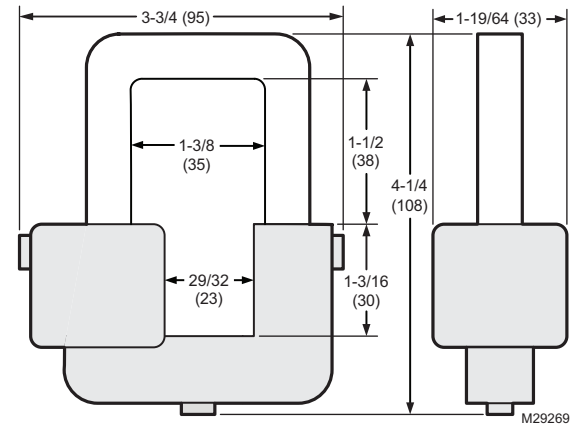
Dimensions du capteur de courant 400 A en po (mm).
